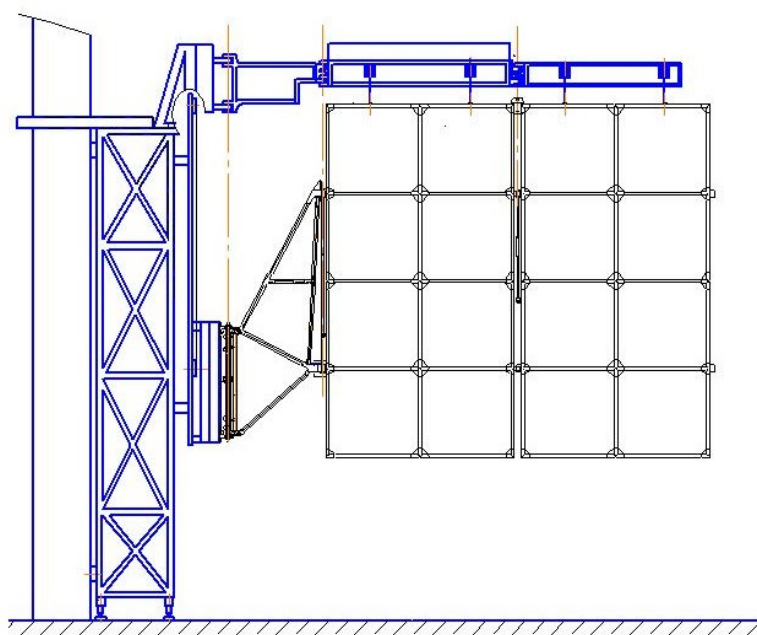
Общий вид стенда раскрытия с панелью БС1 в раскрытом положении
